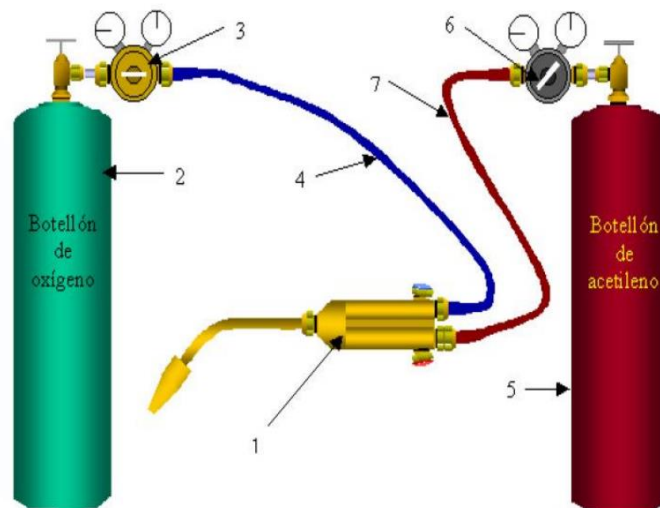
Partes de la soldadura oxiacetilénica [10]
